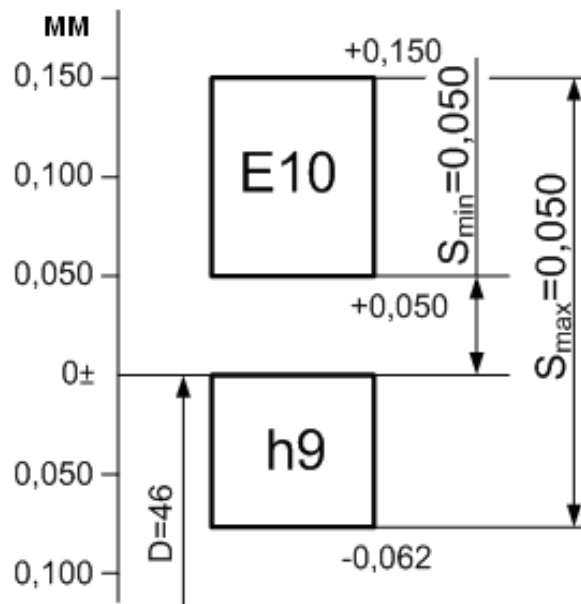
Схема розташування полів допусків деталей з'єднання $\varnothing 46E10/h9$
